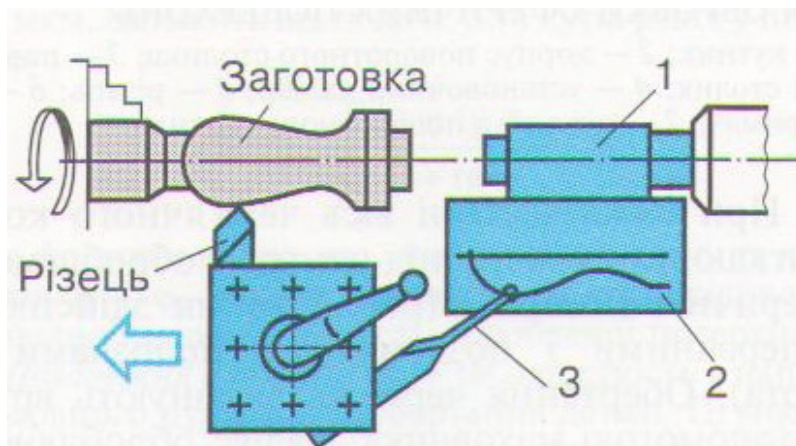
Обробка фасонних поверхонь способом поєднання двох подач з контролем за креслеником:
